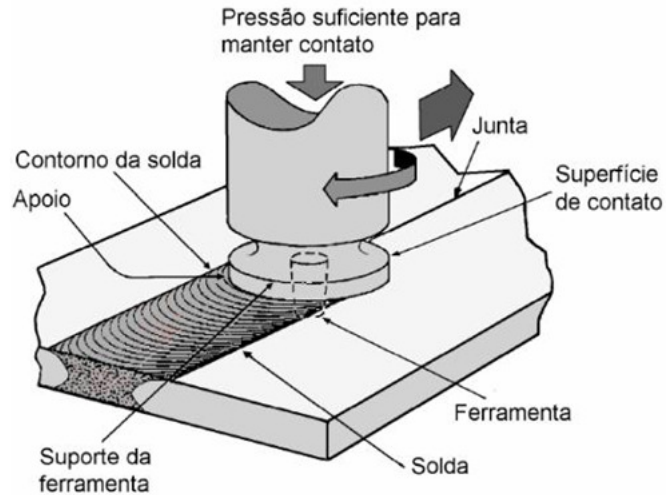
Processo de solda por fricção e mistura<sup>(1)</sup>.
